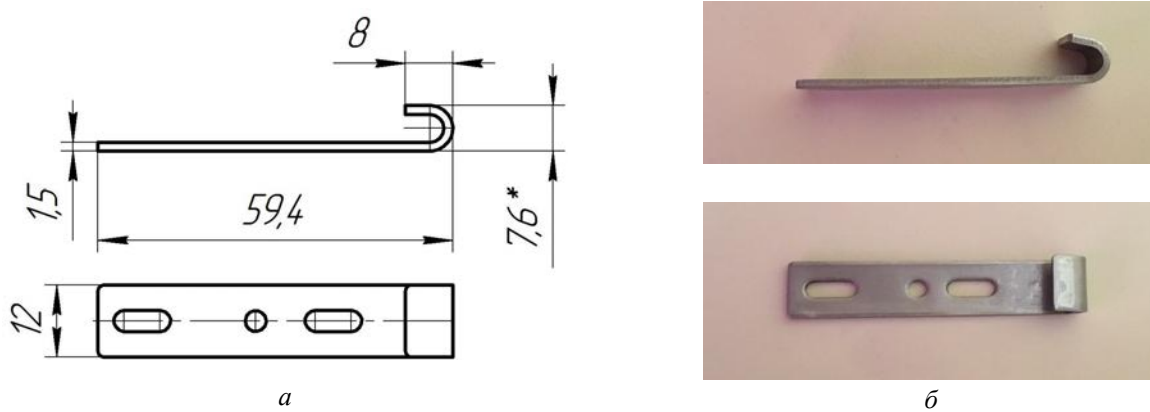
Деталь типу “Гачок”: а – робоче креслення; б – загальний вигляд
